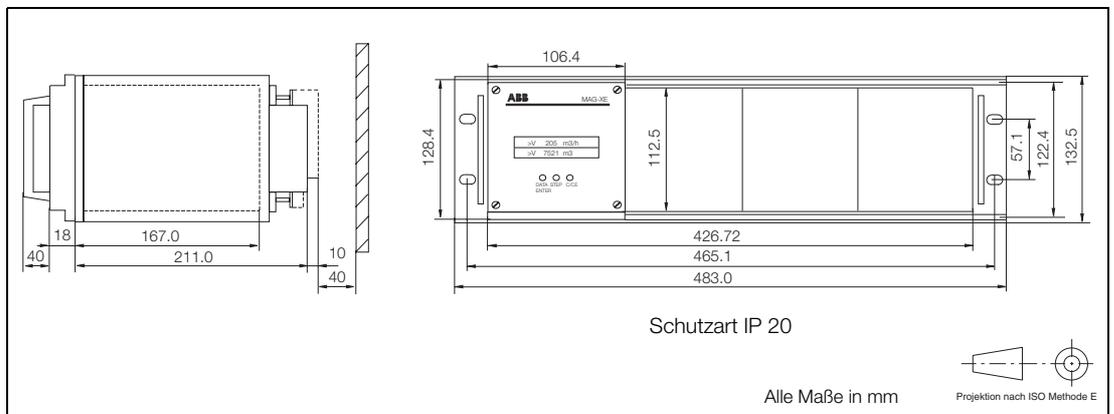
Maßzeichnung 19" Messumformer FXE4000 (MAG-XE) im Baugruppenträger
